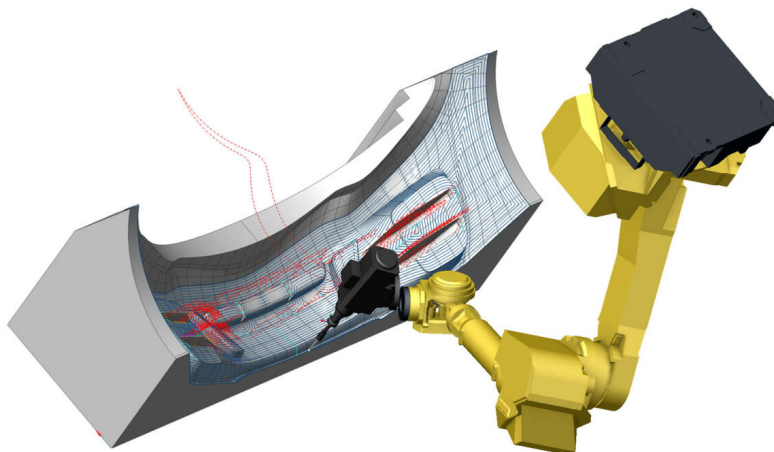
Prostředí Verbotics Weld [24]
